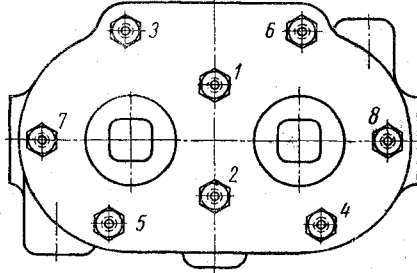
Порядок затягивания гаек шпильки крепления головки блока цилиндров компрессора
